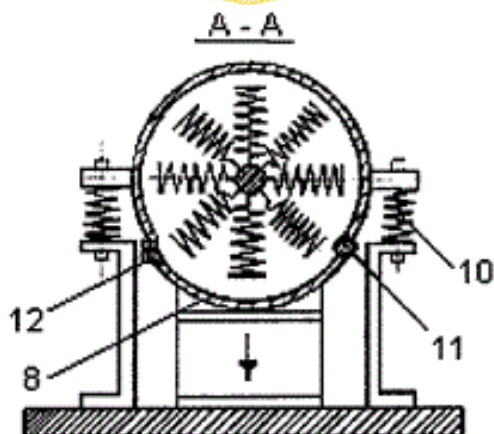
Вибрационный смеситель №1. Сечение А-А: 8 — разгрузочный люк; 10 — пружины; 11 — шарнир; 12 — защелка
